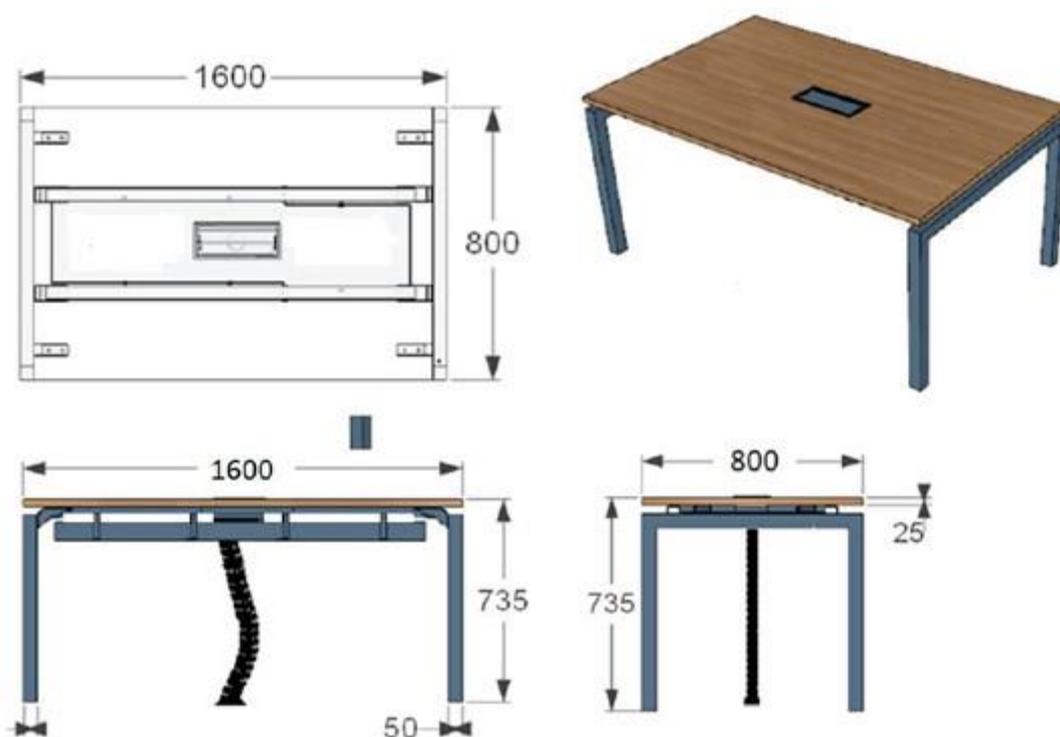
Planta baixa, vista frontal, vista lateral e perspectiva modelo item 22
